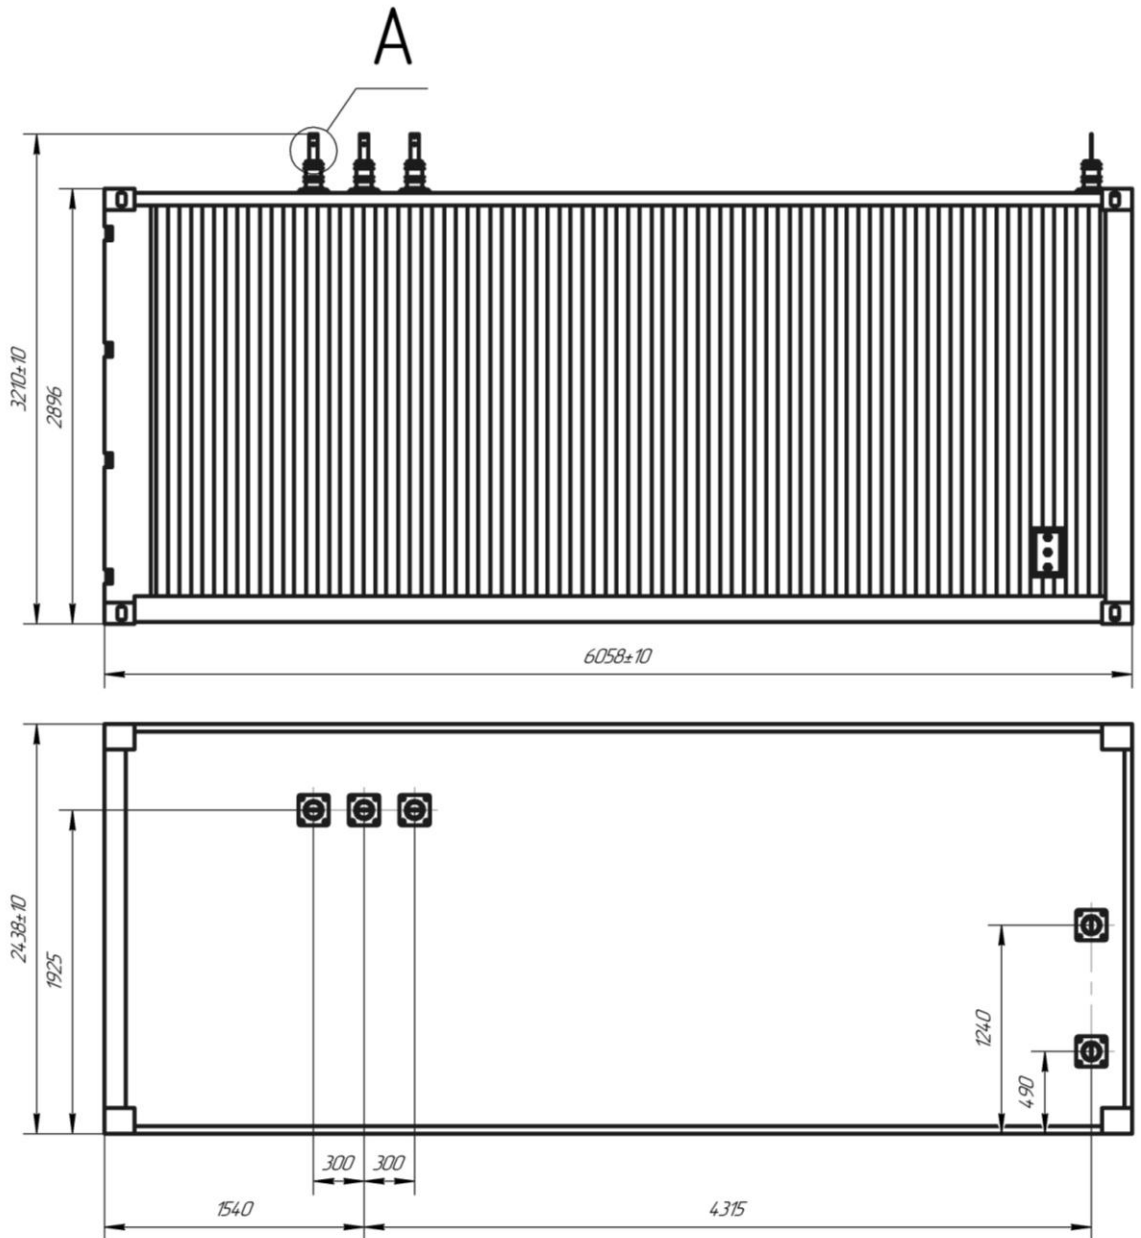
Габаритный чертеж контейнера В-ТПП
